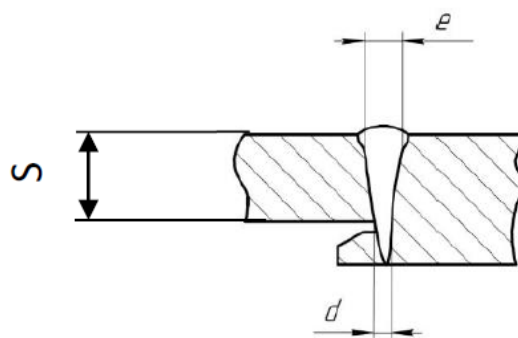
Конструктивные элементы шва сварного соединения
